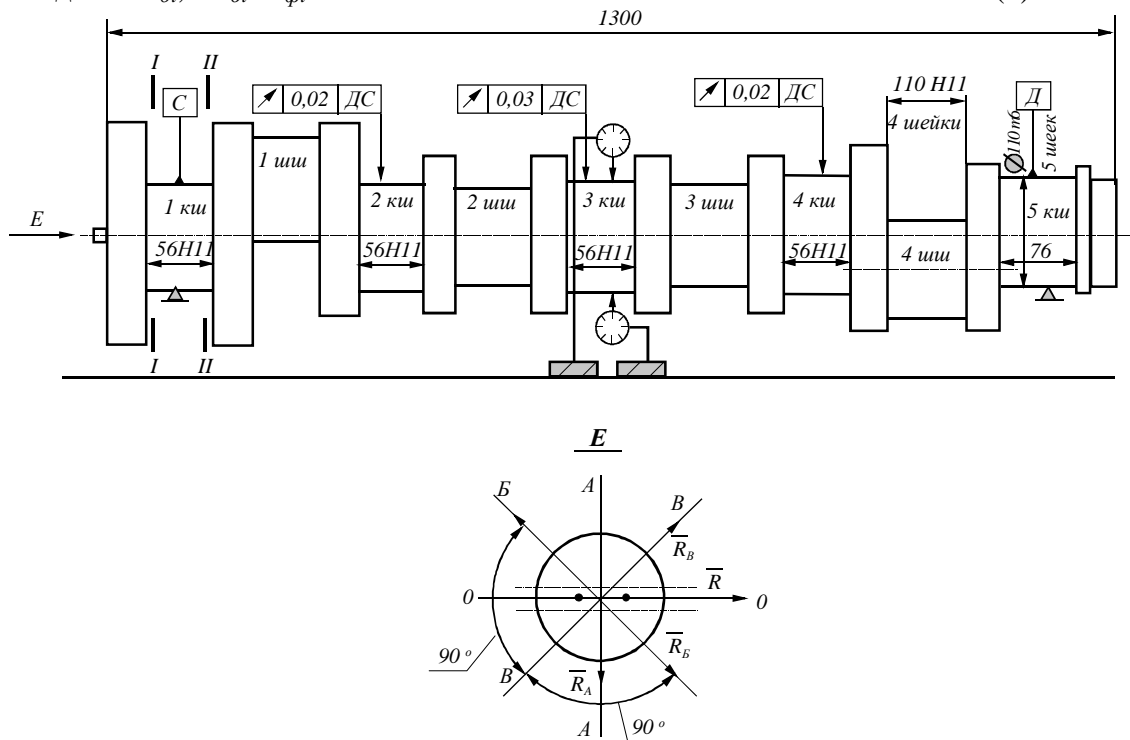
Схема измерения биений коренных шеек вала двигателя
